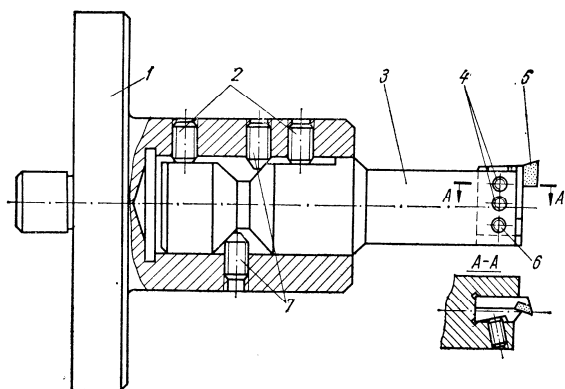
Борштанга для подрезки торцов методом врезания: 1 – корпус; 2 – прижимные винты; 3 – вставка; 4 – прижимные винты резца; 5 – резец; 6 – установочный винт резца; 7 – установочные винты вставки.
